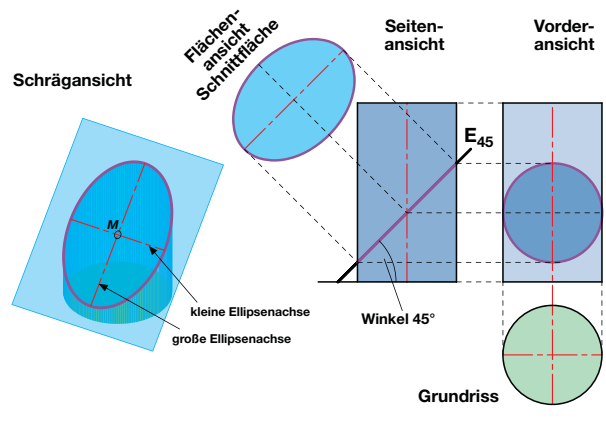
Zylinder mit 45° geneigter Schnittebene: Die Vorderansicht der Schnittfläche entspricht einem Kreis, die Flächenansicht entspricht einer Ellipse!
